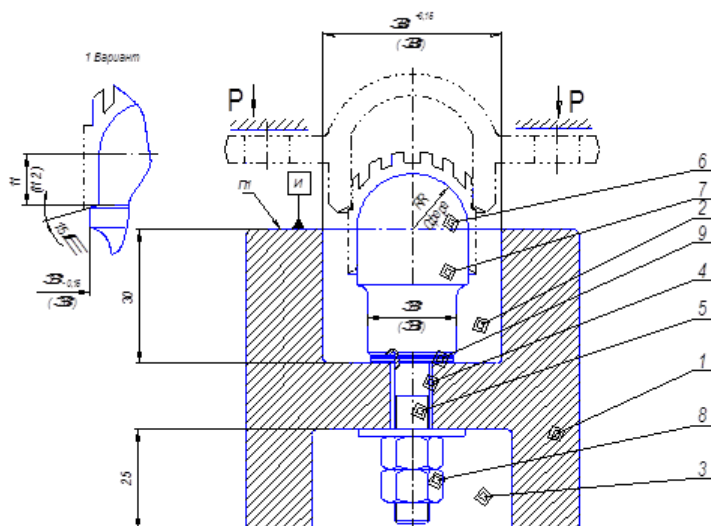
Приспособление для сборки элементов кинематической пары
